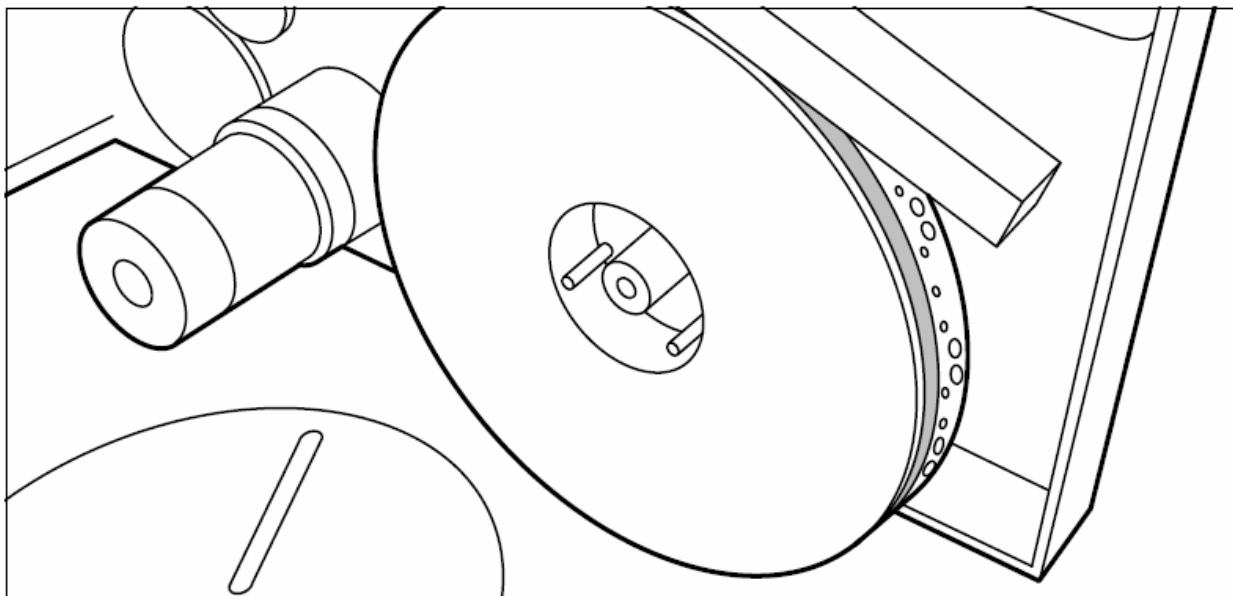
Установка новой катушки с самоклеящейся лентой
